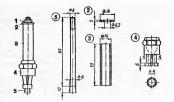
Приспособление для исправления резьбы: 1 — гайка Мб; 2 — шайба; 3 — втулка; 4 — основание; 5 — распорный конус.
